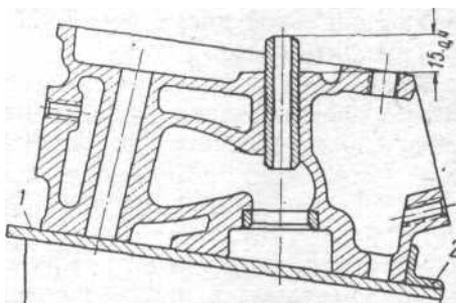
Оправка для выпрессовывания направляющей втулки клапана
